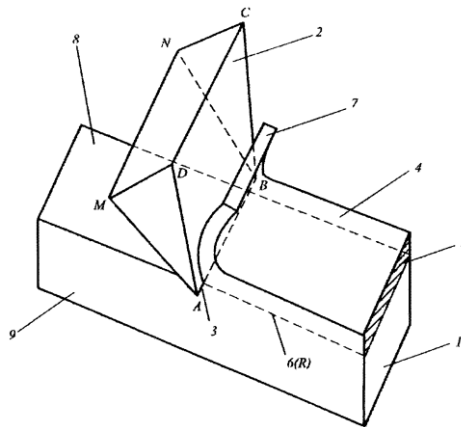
Схема взаємодії леза з заготовкою: 1 - заготовка; 2 - лезо; 3 - різальна кромка; 4 - поверхня, що обробляється; 5 - припуск; 6 - поверхня різання; 7 - стружка; 8 - оброблена поверхня; 9 - оброблена деталь
